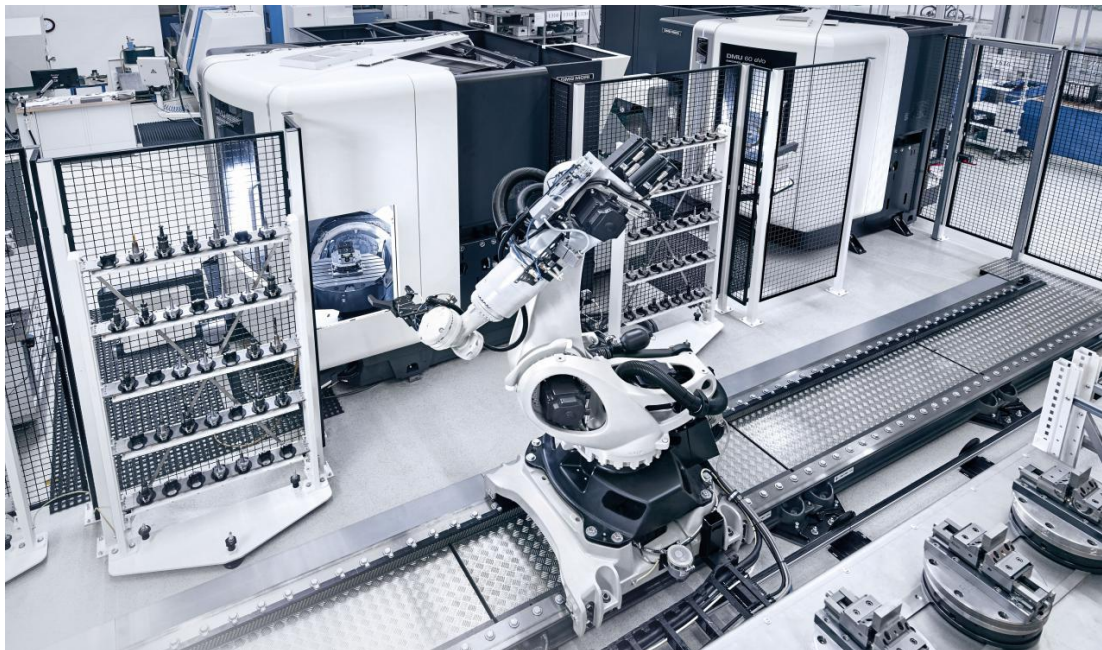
Robot KUKA KR QUANTEC manipuluje s obrobky [9]
